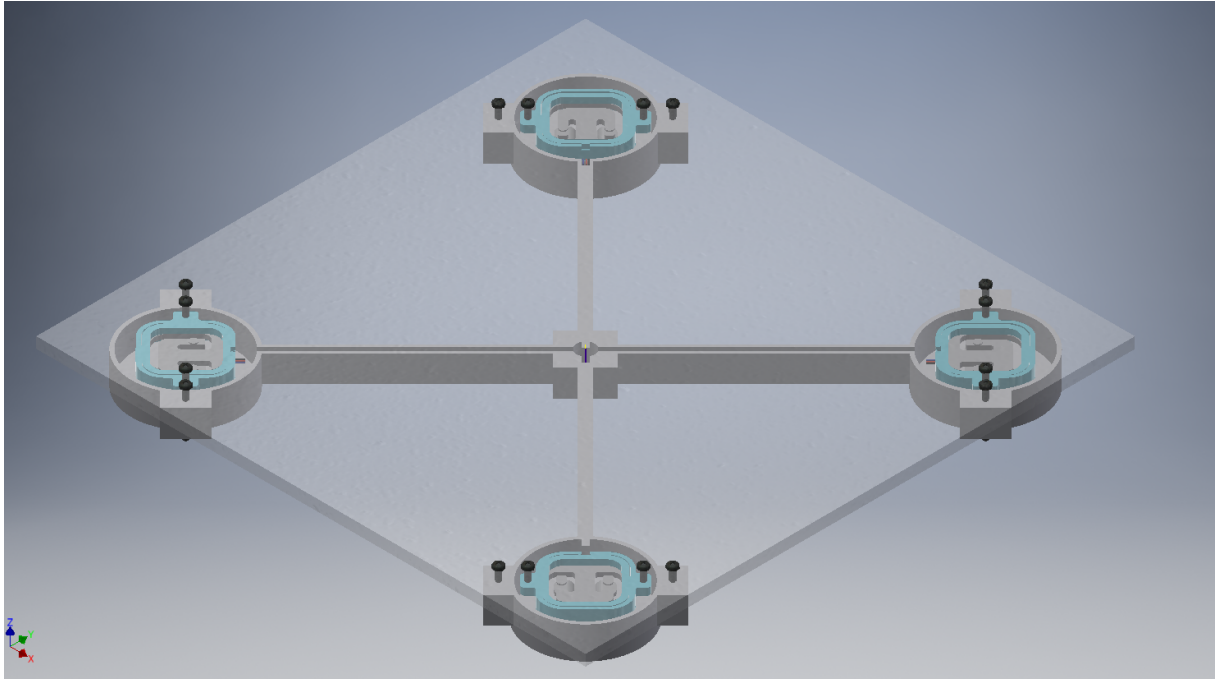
Balanza final con guía para cables. Fuente: Elaboración propia
